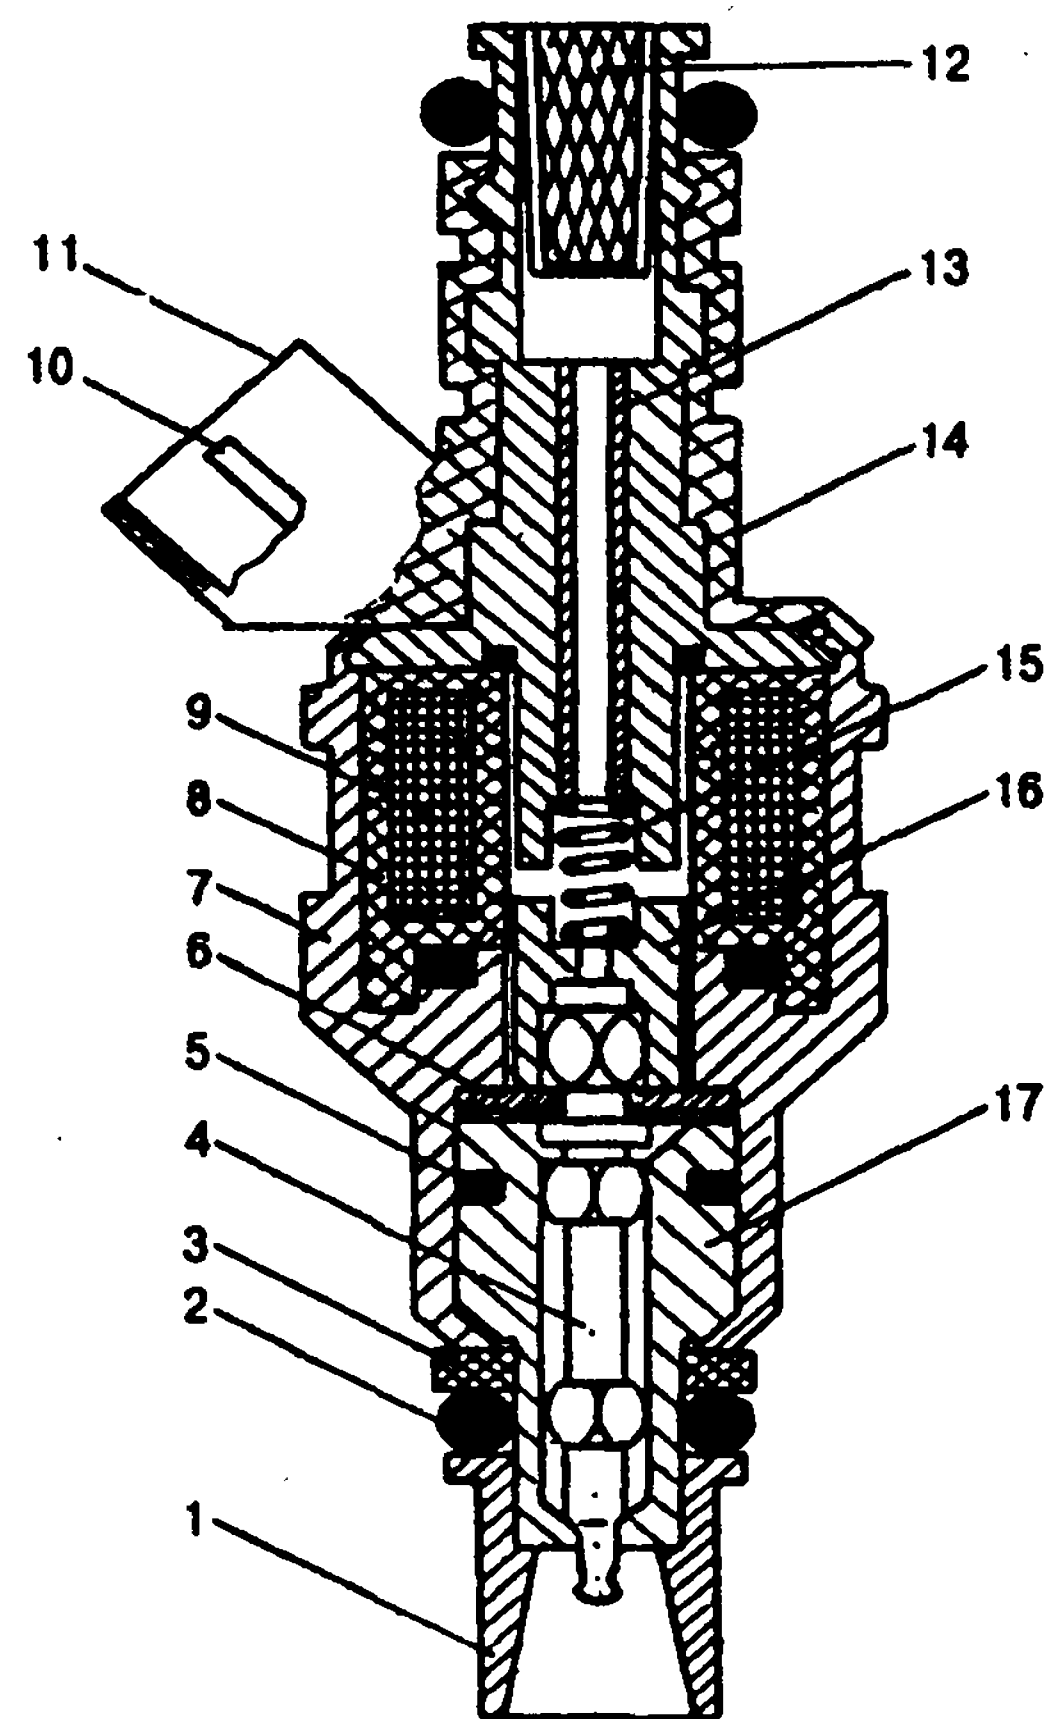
Электромагнитная форсунка: 1 - насадка распылителя, 2 - уплотнительное кольцо, 3 - шайба, 4 - игла клапана, 5 - уплотнитель, 6 - ограничительная шайба, 7 - корпус, 8 - изолятор, 9 - обмотка электромагнита, 10 - штекер, 11 - колодка, 12 - фильтр, 13 - трубка, 14 - крышка, 15 - пружина, 16 - сердечник электромагнита, 17 - корпус клапана-распылителя
